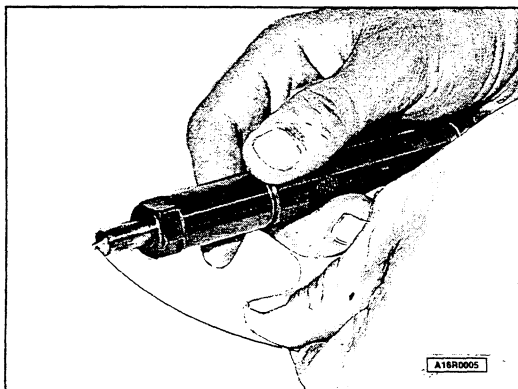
Limpieza del inyector mediante alambre armónico.
